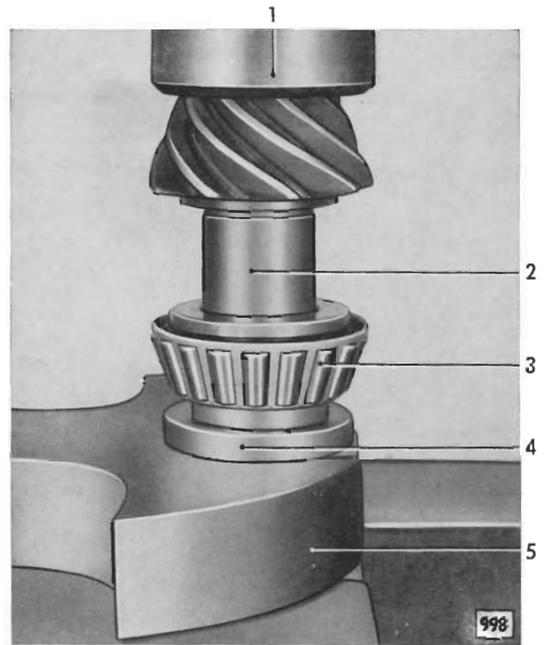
Inneren Laufring mit Kegelkäfig des inneren Lagers auf Antriebkegelrad aufpressen
